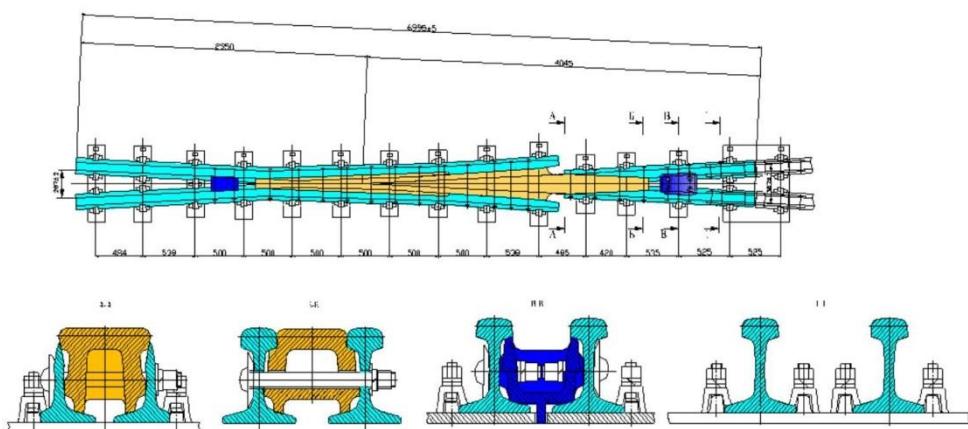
Чертеж крестовины перевода КС6511-03.00.000
